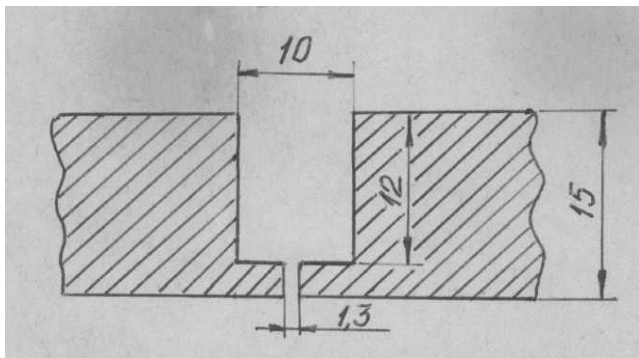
Схема розробки під зварювання кришки 6Ч25-34
